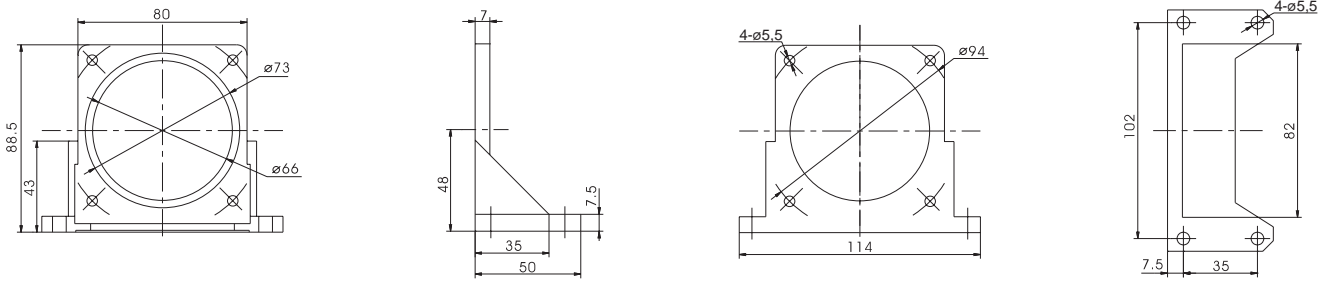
Befestigungsflansch BFM 80 | Fig. 1 : Mounting bracket BFM 80
